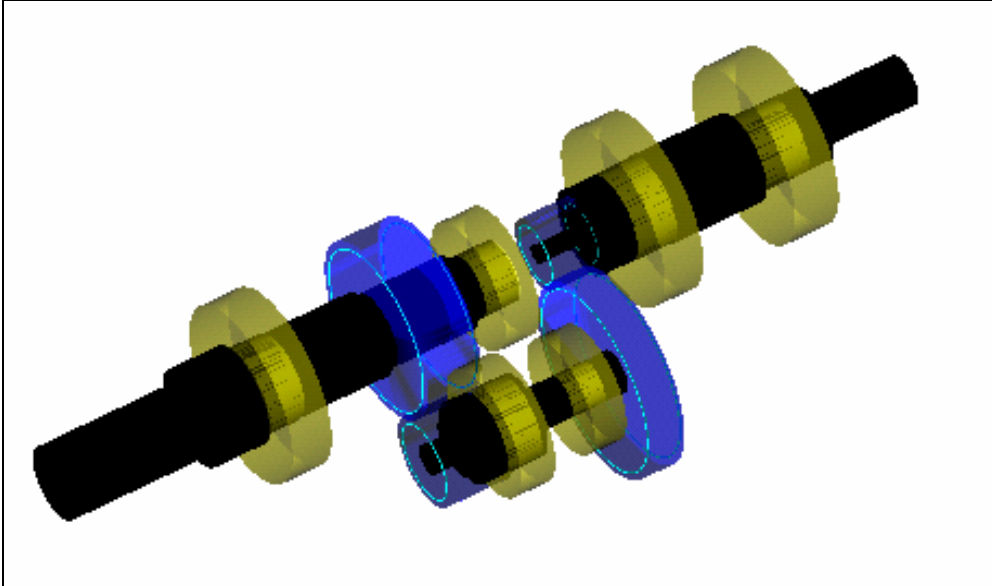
Aufbau des Getriebes: Schwarz: Wellen, Blau: Zahnräder, Gelb: Wälzlager
